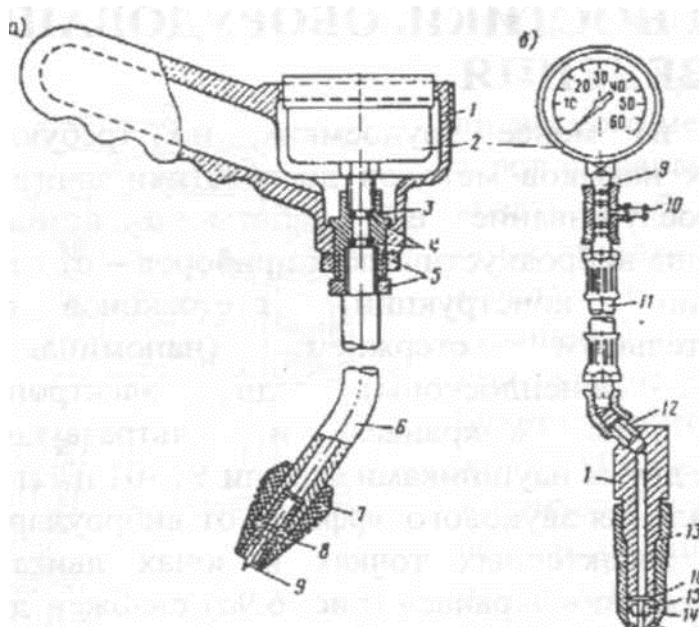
Компрессометры: а - для карбюраторных двигателей; б - для дизелей; / - корпус; 2 - манометр; 3 - штуцер; 5 - контргайки; б - трубка; 7 - резиновый наконечник; 8 - золотник; 10 - выпускной клапан; 11 - шланг; 12 - переходник; 13 - зажимная гайка; 14 - клапан; 15- пружина клапана; 16-седло; 17 - наконечник
